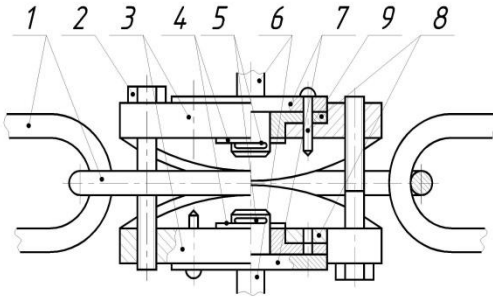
Борона гнучка з регульованими зубами (робоча одиниця):
